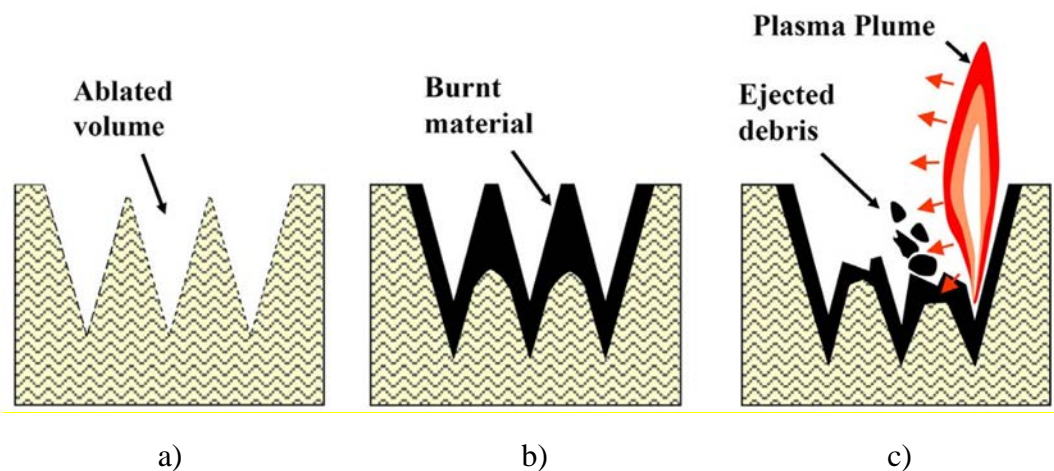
Principali meccanismi di rimozione del materiale: a) ablazione; b) combustione; c) effetto meccanico [59].
